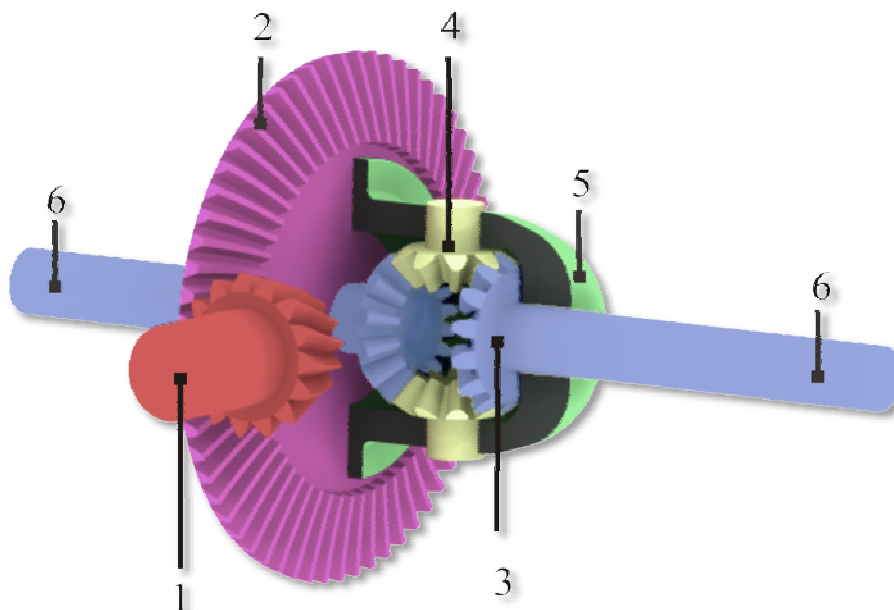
Soukolí typu  $2k+r$  [5]
